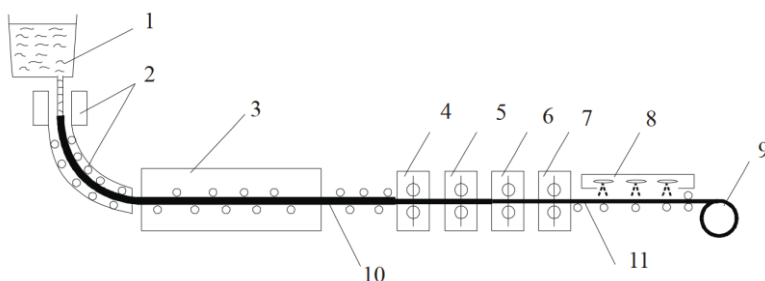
Ливарно-прокатний комплекс з МБЛЗ
